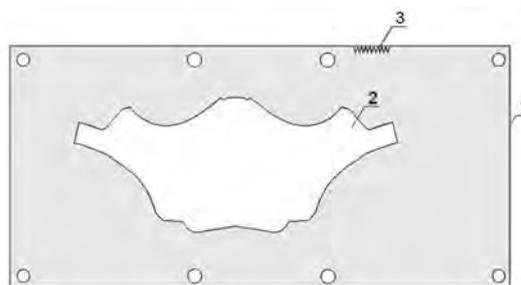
Заготовка технологической оснастки для деталей верха самого большого размера:
